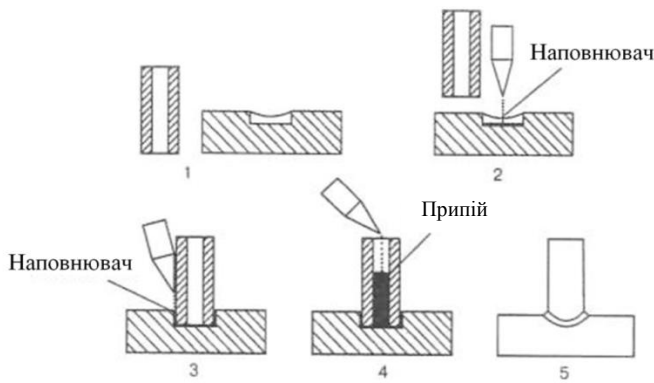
Схема складання деталей для з'єднання просоченням розплавом наповнювача в широкому зазорі: 1 – деталі перед складанням; 2 – заповнення стикової частини з'єднання наповнювачем; 3 – заповнення телескопічної частини наповнювачем; 4 – заповнення технологічної порожнини металом матриці; 5 – вузол після просочення
